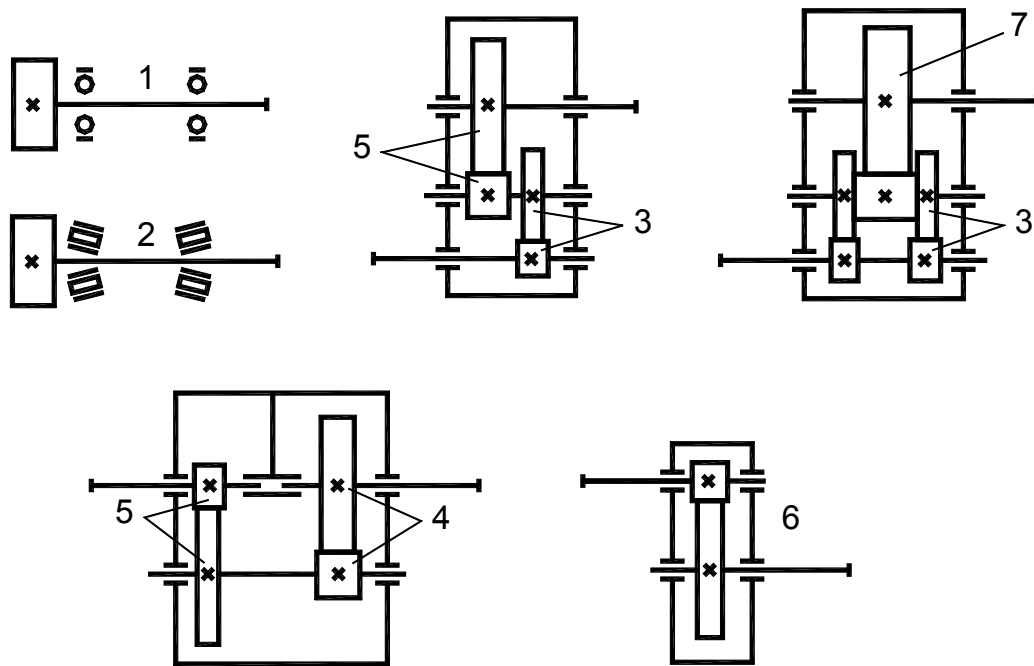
Схемы расположения колес в цилиндрических редукторах
